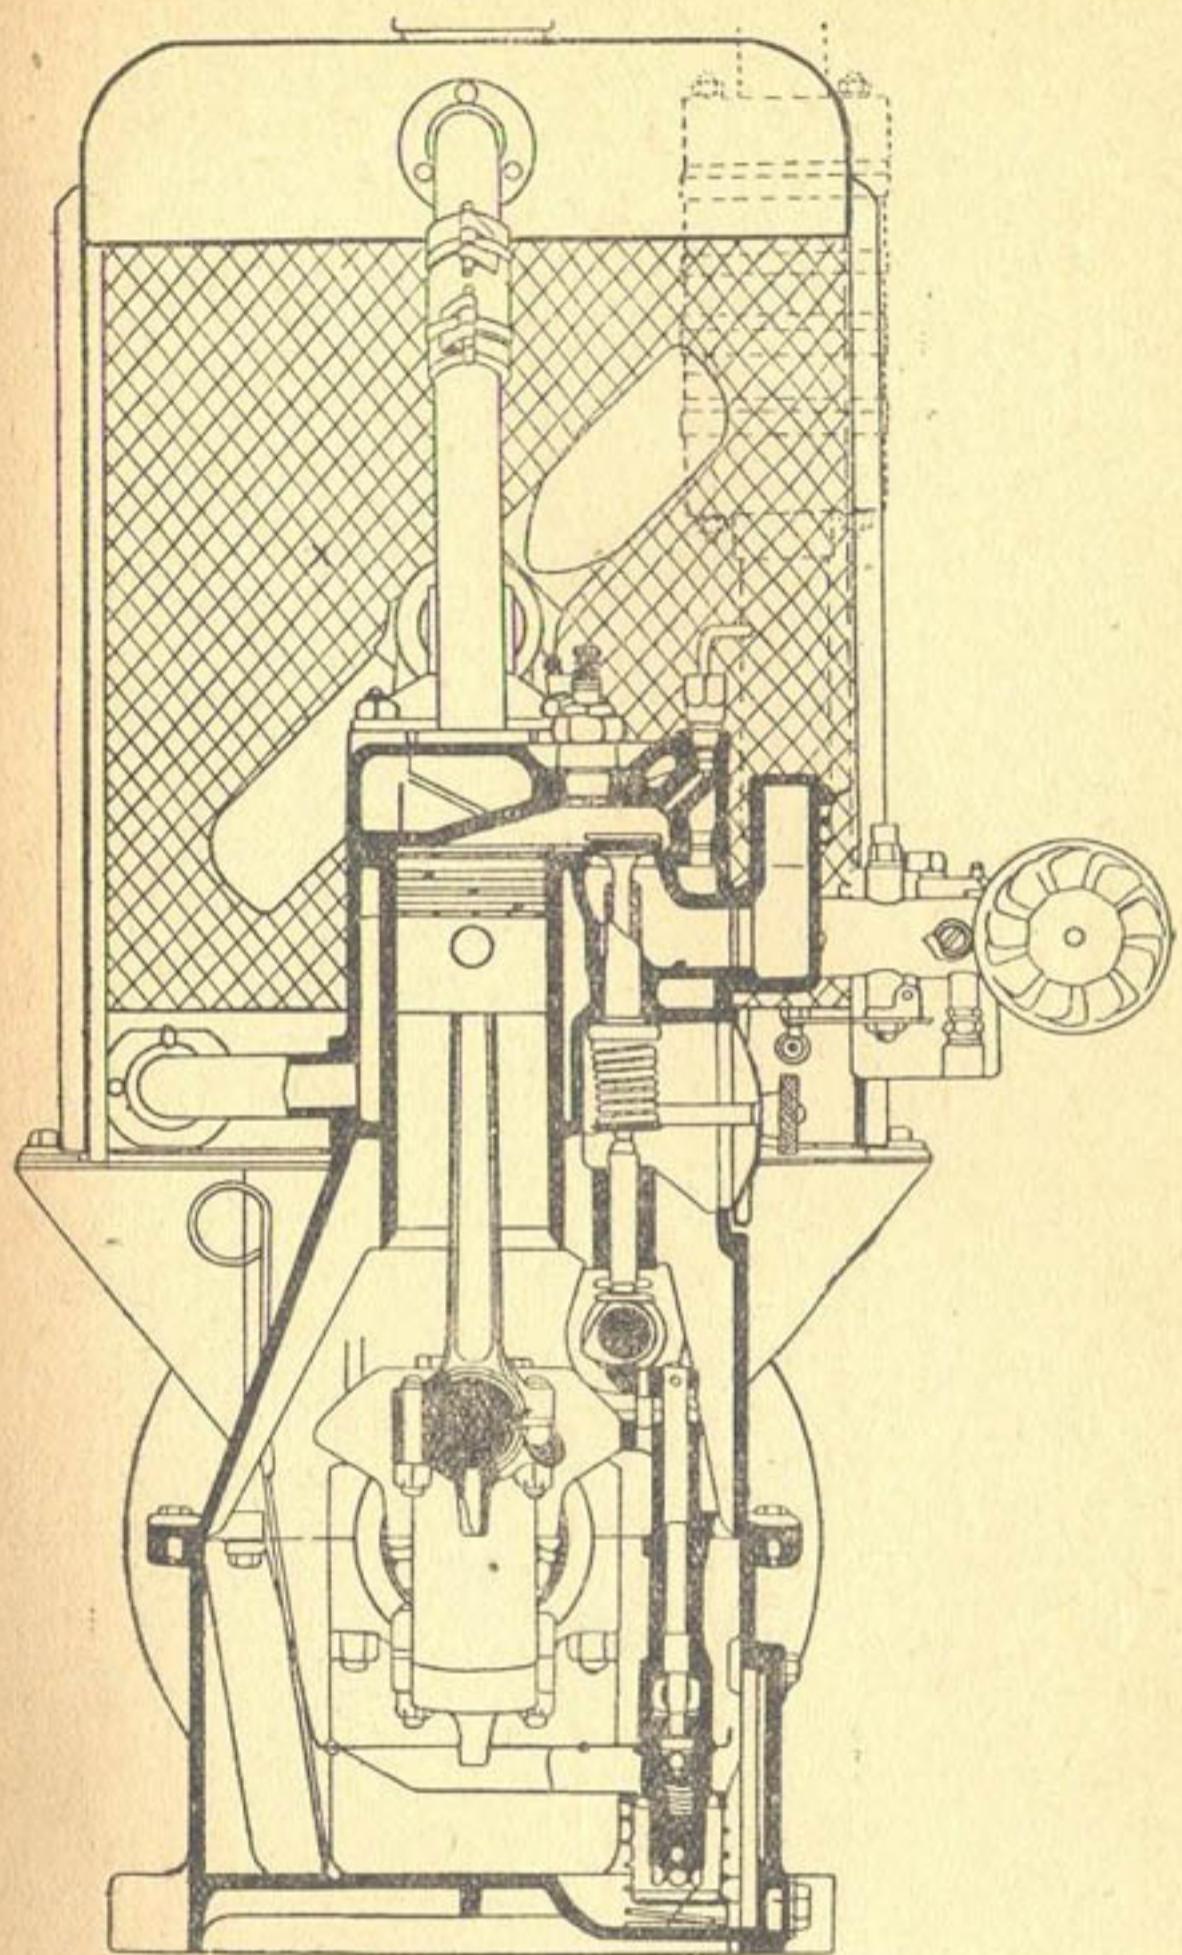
Общий вид бензинового двигателя ЛД-6.
